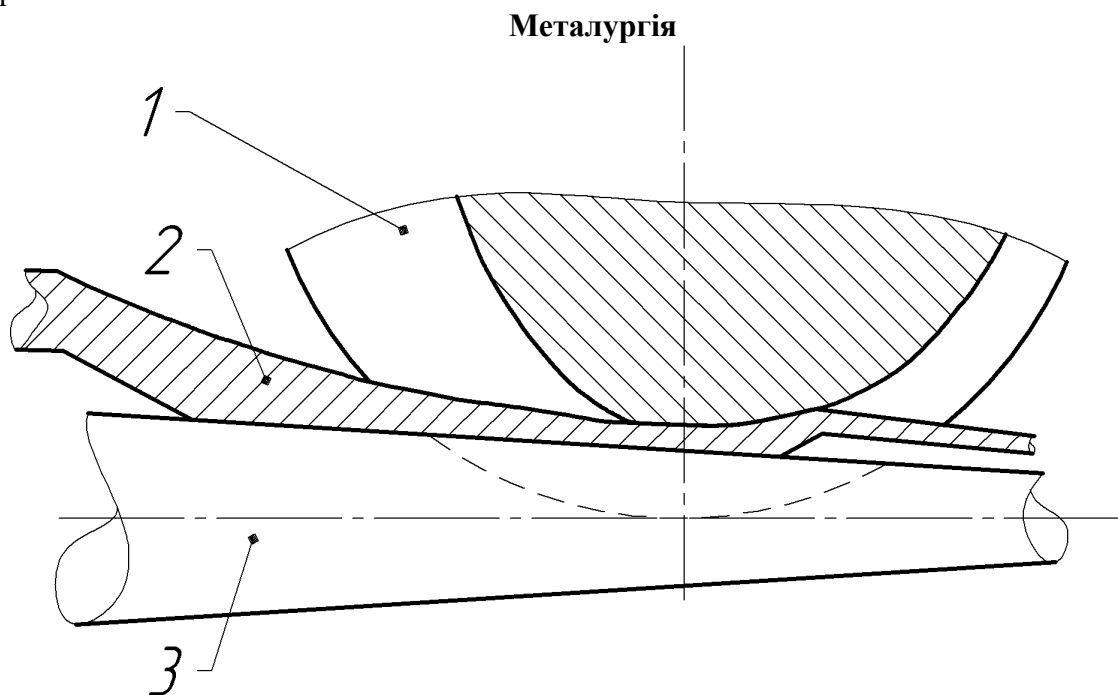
Схема процесу холодної періодичної валкової прокатки на стані типу ХПТ: 1 – валок, 2 – робочий конус деформування, 3 – оправка
